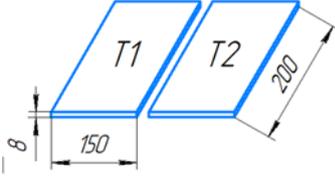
Пластины, подготовленные для сварки
